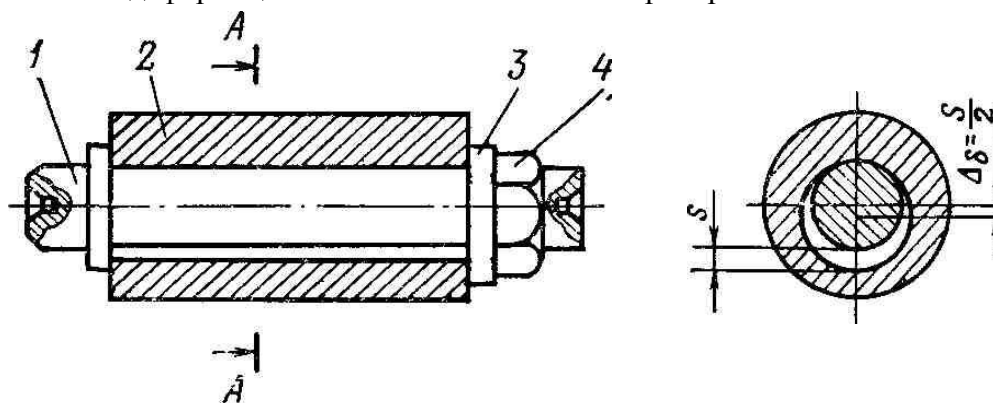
Схема образования погрешности базирования при установке заготовки на цилиндрической оправке с зазором:
